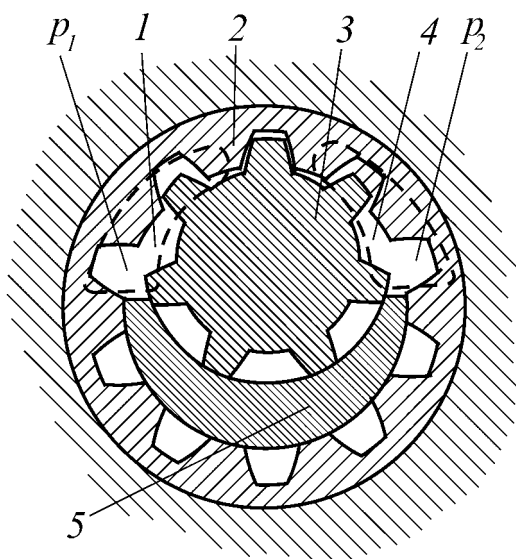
Шестеренная гидромашина с внутренним зацеплением: 1, 4 – подводящая и отводящая полости; 2 – охватывающая шестерня; 3 – внутренняя шестерня; 5 – уплотняющий серпообразный элемент
